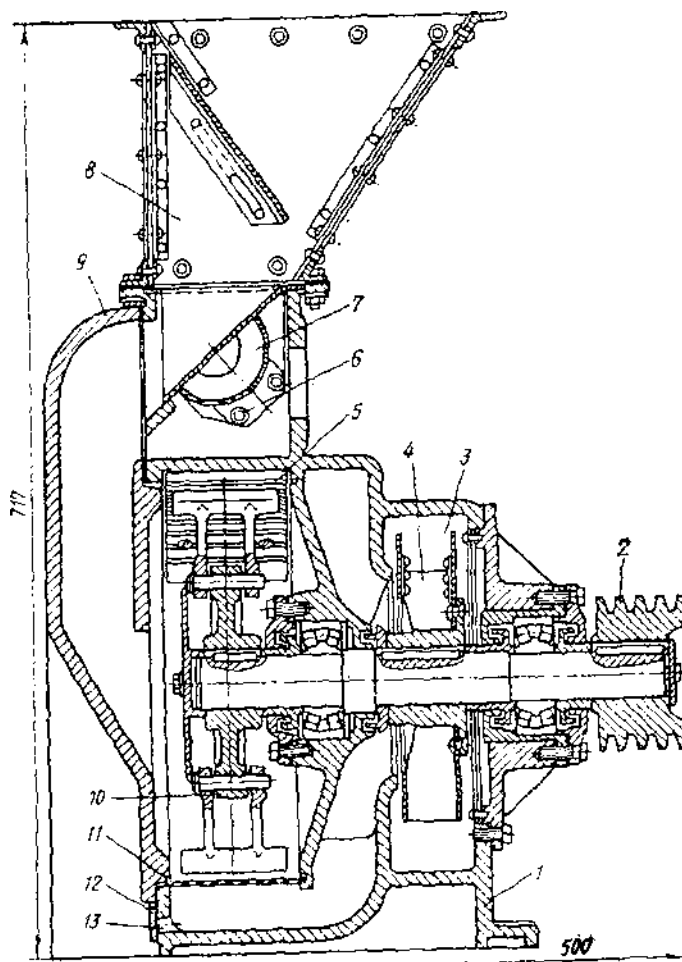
Молотковая дробилка: 1 - корпус; 2 - шкив; 3 - камера для вентиляторного колеса; 4 - вентиляторное колесо; 5 - неподвижная дека; 6 - коробке для магнитов; 7 - постоянные магниты; 8 - приемный бункер; 9 - крышка; 10 - ротор; 11 - сито; 12 - планка; 13 - щель подачи воздуха
